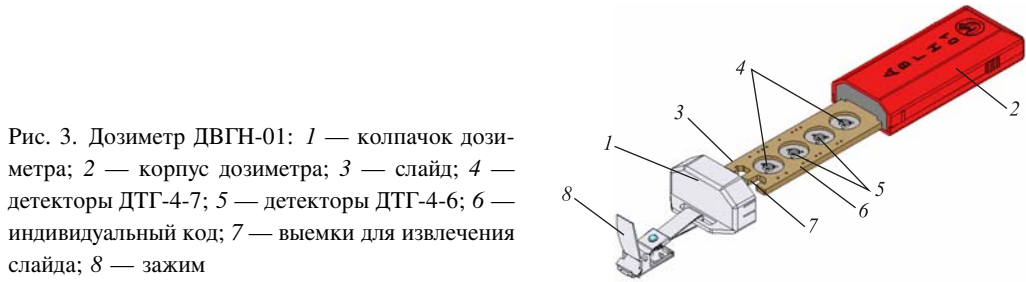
Дозиметр ДВГН-01: 1 — колпачок дозиметра; 2 — корпус дозиметра; 3 — слайд; 4 — детекторы ДТГ-4-7; 5 — детекторы ДТГ-4-6; 6 — индивидуальный код; 7 — выемки для извлечения слайда; 8 — зажим
